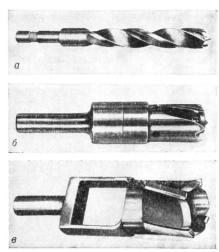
Свёрла для обработки древесины и древесных материалов: а — спиральное с направляющим центром и подрезателем; 6 — цилиндрическое полое с выталкивателем (для высверливания пробок); ϵ для кольцевого сверления.
